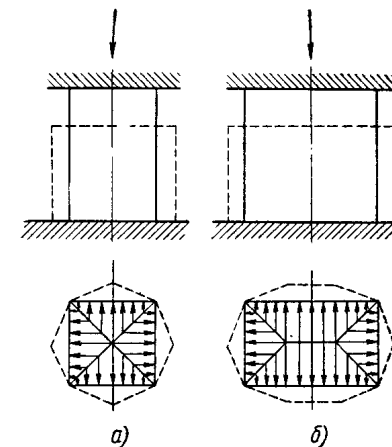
Схема течения металла при свободной осадке образцов: а — квадратного сечения, б — прямоугольного сечения
